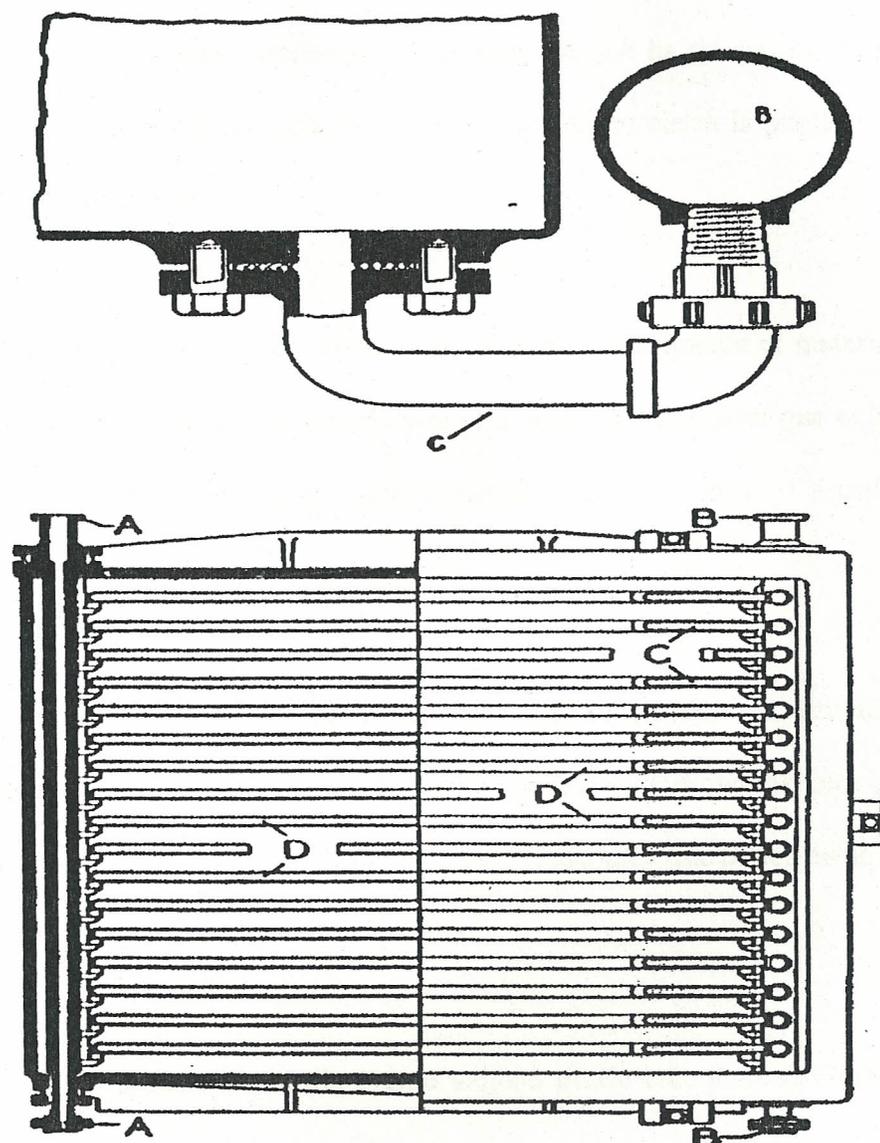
Secadero de vacío: A, tubería de entrada del vapor de agua; B, tubería de salida del condensado; C, conexiones de las estanterías con las tuberías; D, estanterías.
